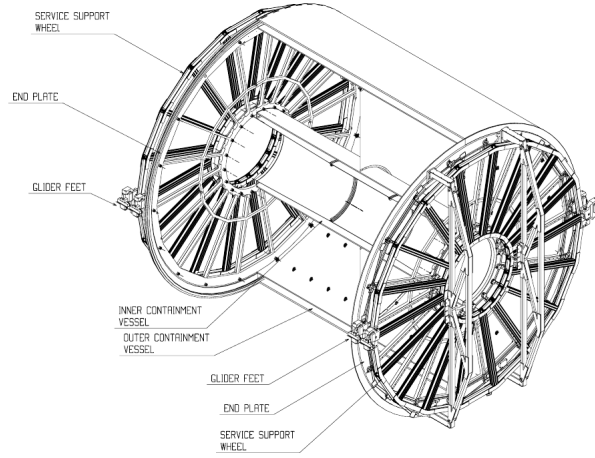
Vista 3D de la caja cerrada de campo TPC y las ruedas de soporte de servicio, sin cámaras de lectura.
